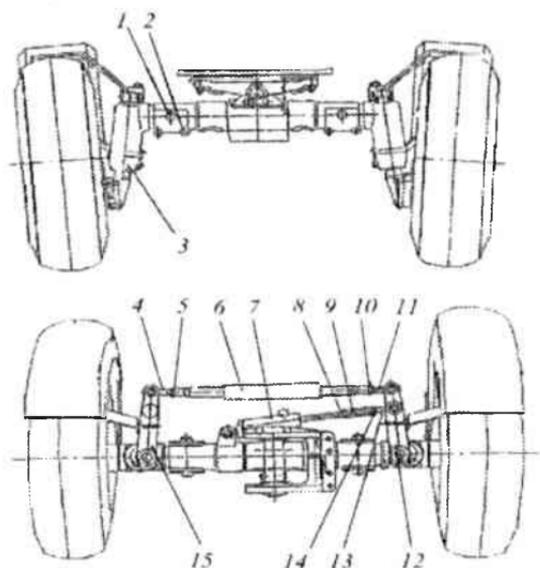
Двухколесный передний мост: 1 – ось; 2 – болт; 3 – кронштейн выдвижной; 4, 11 – шарнир; 5, 8, 10, 14 – контргайка, 6 – тяга, 7 – гидроцилиндр исполнительный; 9 – гайка; 12 – рычаг поворотный левый; 13 – наконечник гидроцилиндра; 15 – рычаг поворотный правый
